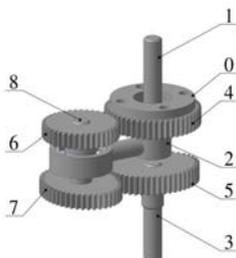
Планетарный механизм с эллиптическими колесами
